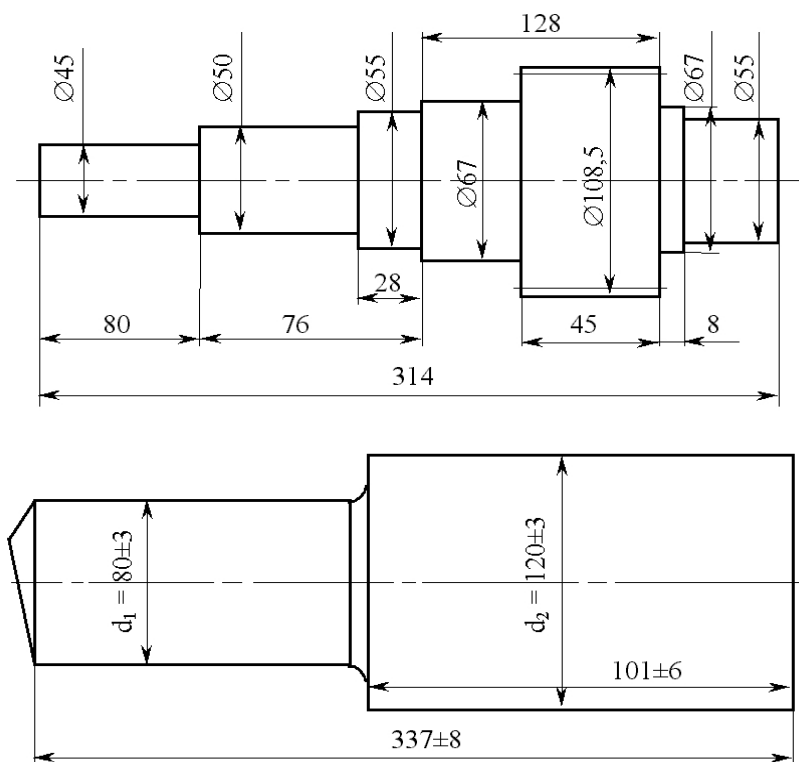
Вид детали и заготовки с припусками на поковку
